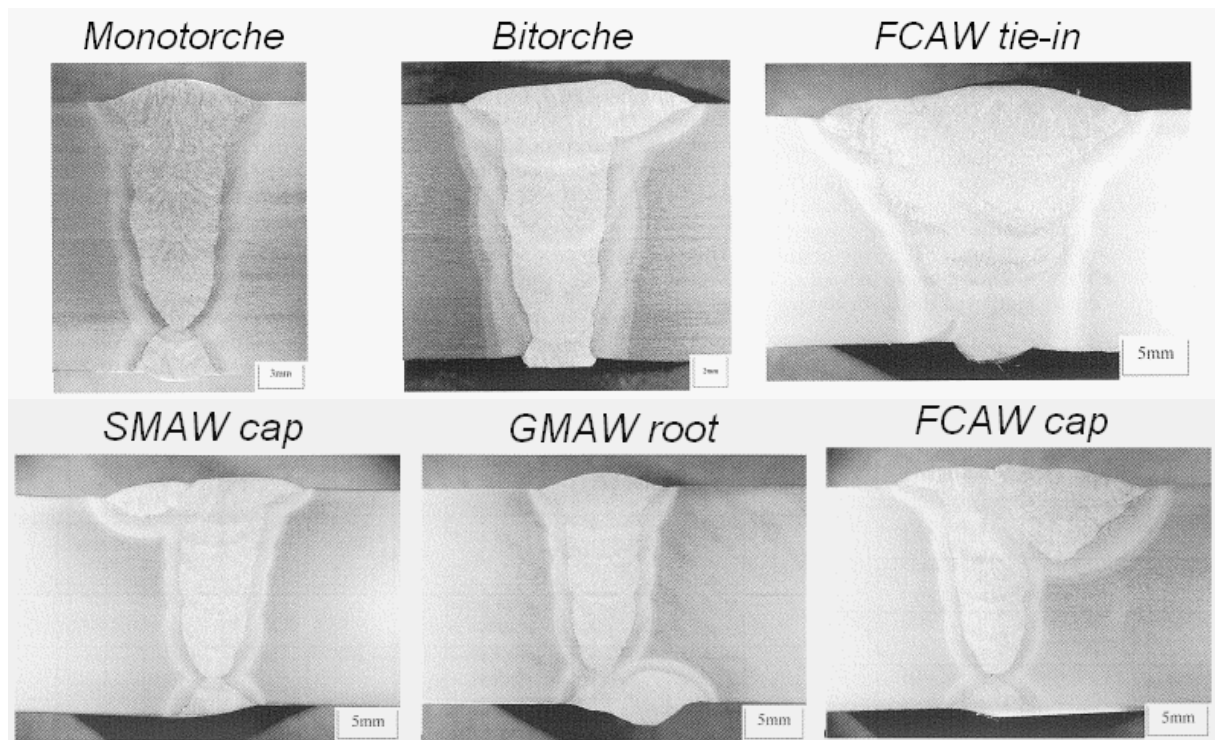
Coupes macroscopiques des soudures de SERIMAX et du WERC [HAMM02-PDC]
